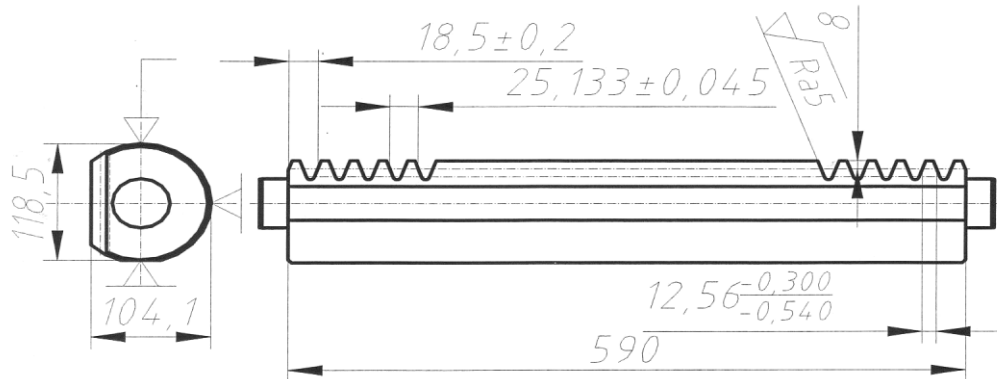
Ескіз обробки деталі операція №055
